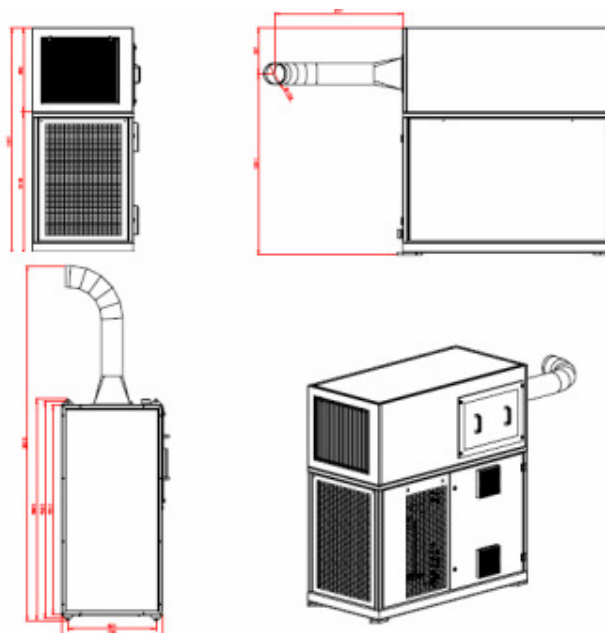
Exemplo de Desenho Dimensional Parcial
